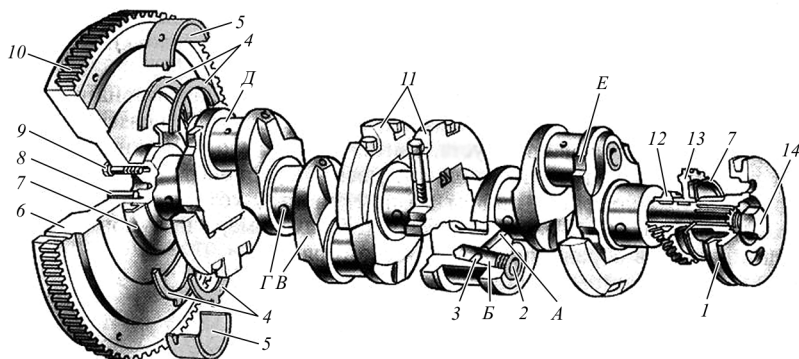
Коленчатый вал двигателя Д-245 с сопряженными деталями: *А* – канал подвода масла; *Б* – полость центробежной очистки масла; *В* – щеки кривошипа; *Г* – коренные шейки коленчатого вала; *Д* – шатунные шейки коленчатого вала; *Е* – галтель; *1* – шкив; *2* – пробка; *3* – трубка; *4* – упорные полукольца; *5* – вкладыш коренного подшипника; *6* – маховик; *7* – маслоотражатель; *8* – установочный штифт; *9* – болт крепления маховика; *10* – зубчатый венец; *11* – противовесы; *12* – шестерня коленчатого вала; *13* – ведущая шестерня привода масляного насоса; *14* – болт для проворачивания вала
